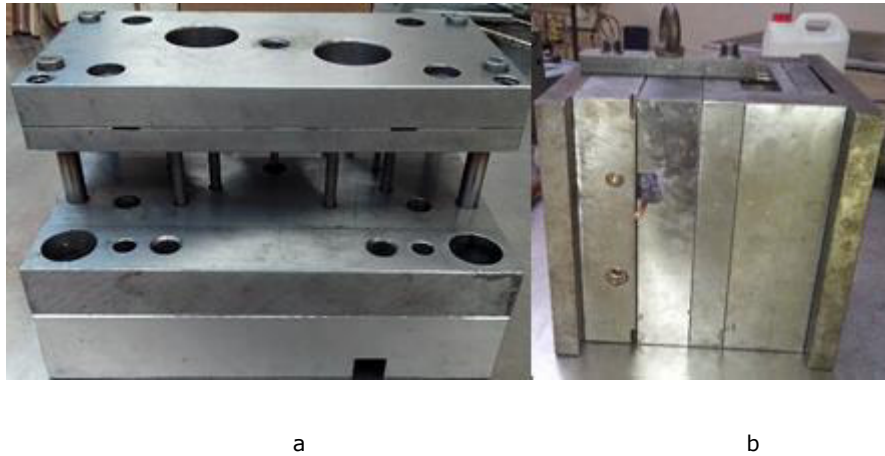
a – Chapa de aperto dos extratores, chapa dos extratores, chapa de reforço da bucha, chapa da bucha; b – molde montado
